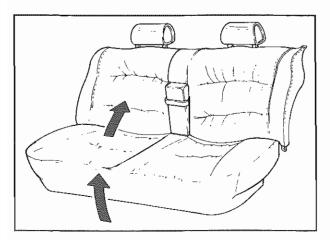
II pianale si smonta sollevandolo anteriormente con una mano The seal bottom can be removed by lifting the I. part with a hand
